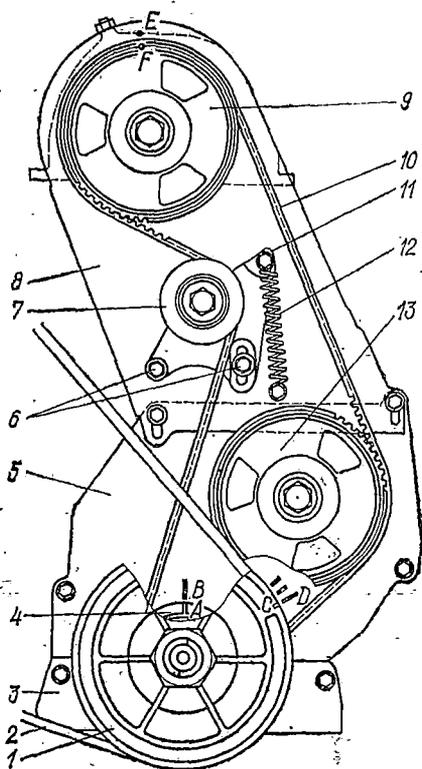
Схема привода механизма газораспределения зубчатым ремнем:
